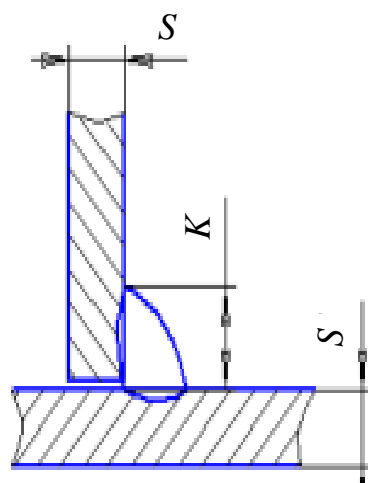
Схема зварного з'єднання автозчепи Т1-Δ4, зварний шов № 1
